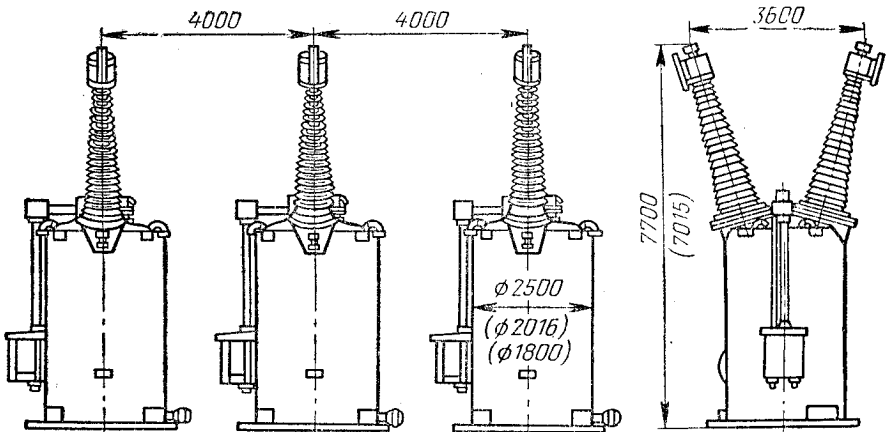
Выключатель У-220-10 (в скобках больший размер для У-220-15, меньший для С-220-25).
